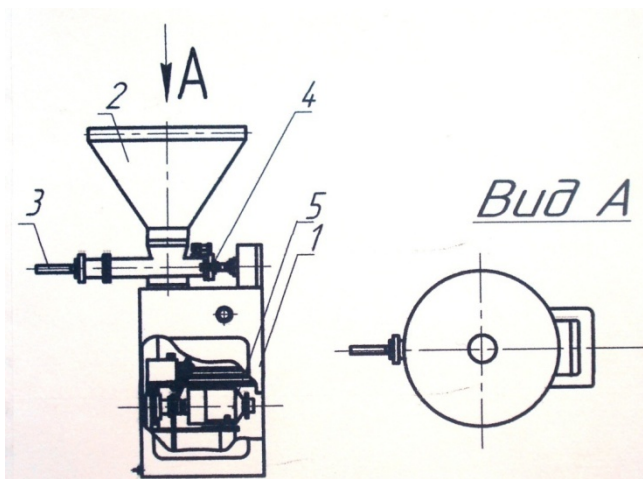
Шприц ФШ2-ЛМ непрерывного действия: 1 – сварная станина; 2 – приемная воронка; 3 – дозирующее устройство; 4 – вакуумная система (разрежение 80 кПа); 5 – электродвигатель.
